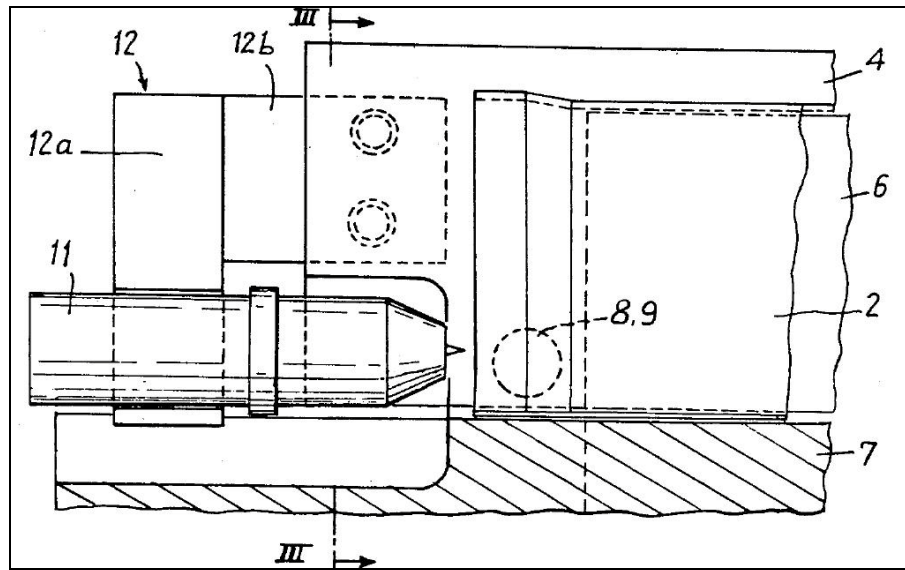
Esquema de una Máquina plegadora y soldadora de aristas [8]
